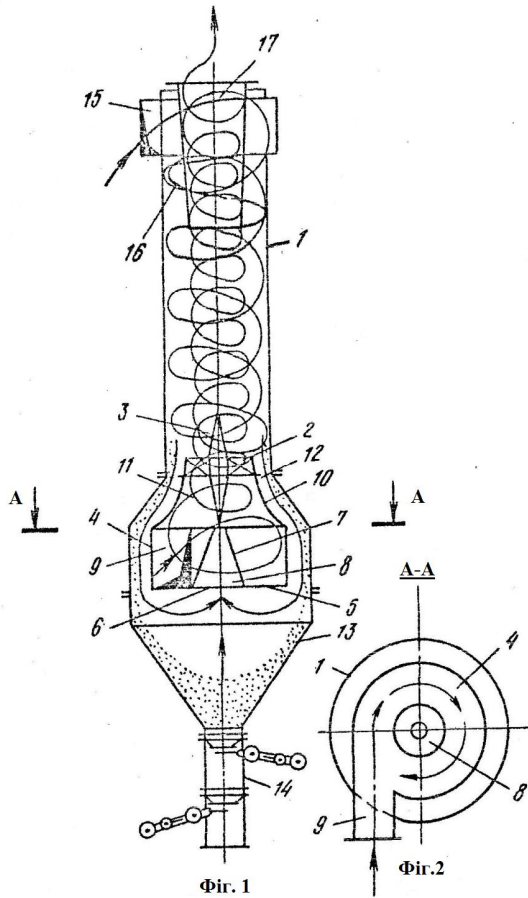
Вихровий пилов-ловлювач з основним потоком у приосьовому завихровувачі й допо-міжним периферійним потоком: 1 – корпус; 2 – завихровувач; 3 – обтікач; 4 – камера; 5 – дно; 6 – конус; 7 – осьовий корпус; 8 – осьовий конус; 9 – тангенціальний патрубок; 10 – циліндрично-конічна стінка; 11 – порожнина; 12 – кільцева порожнина; 13 – бункер; 14 – пиловий затвір; 15 – равликовий завихровувач; 16 – гвинтова направляюча; 17 – вихідна труба
